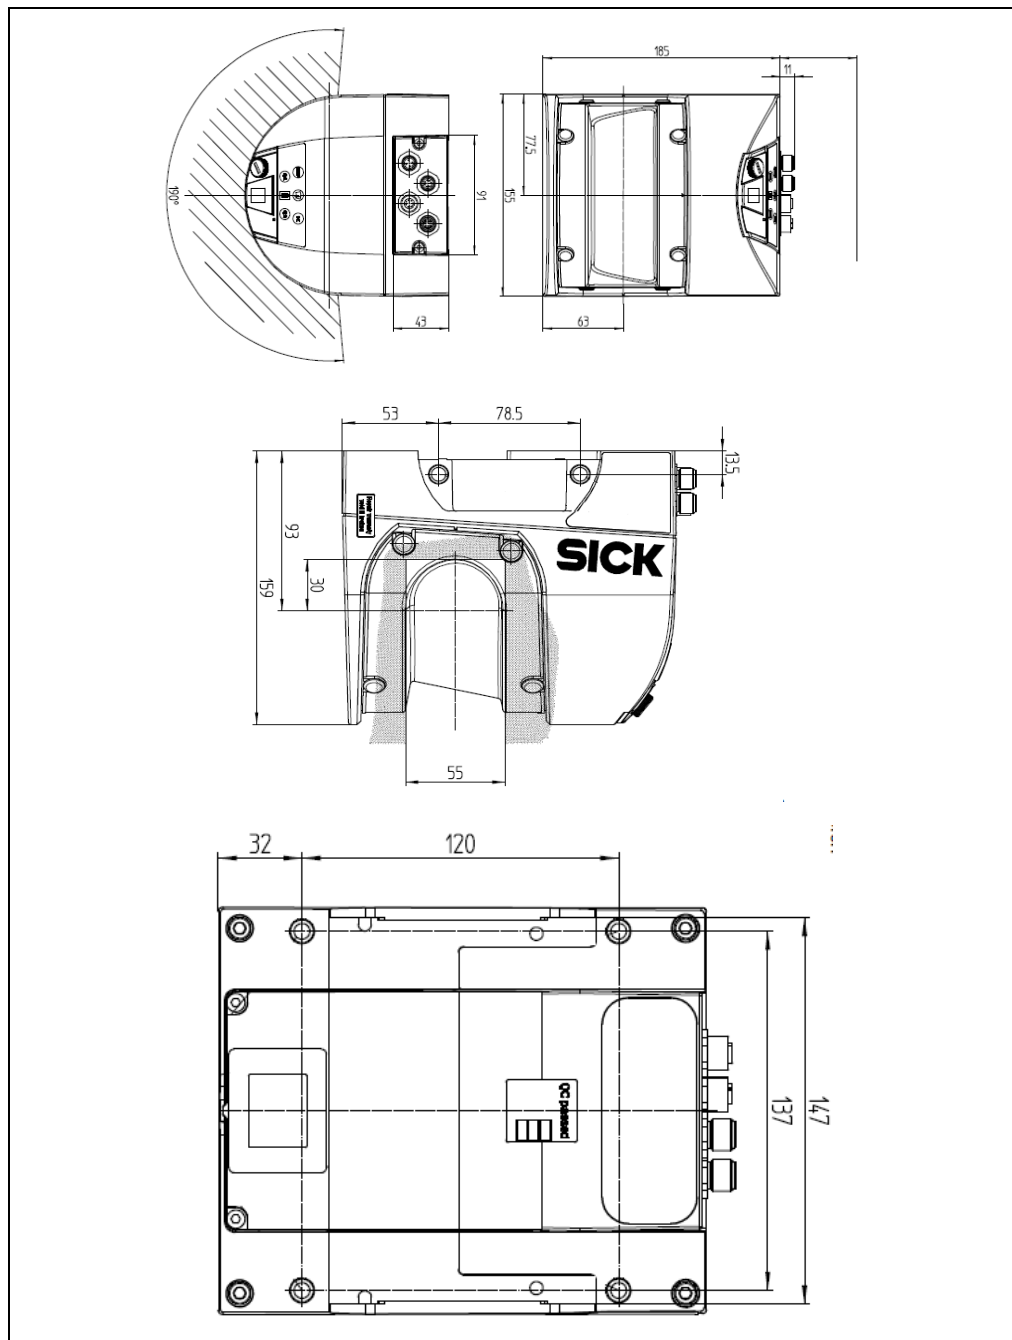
Dimensional drawing for the LMS511 SE 2D LiDAR sensor
